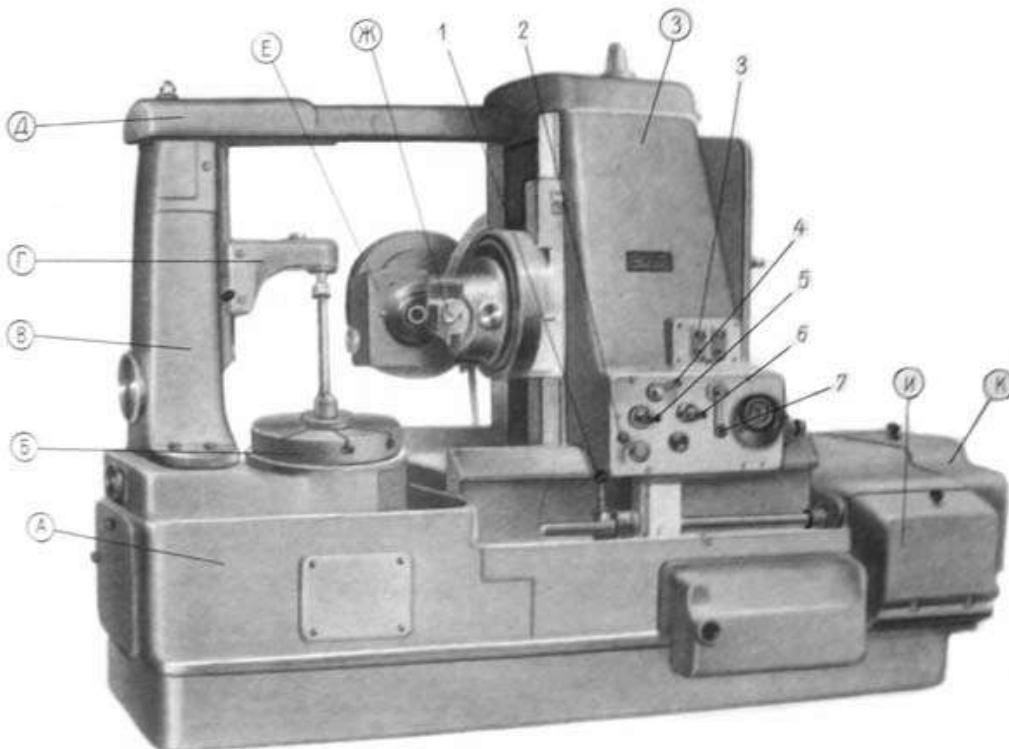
Загальний вигляд зубофрезерного верстата моделі 5Д32
